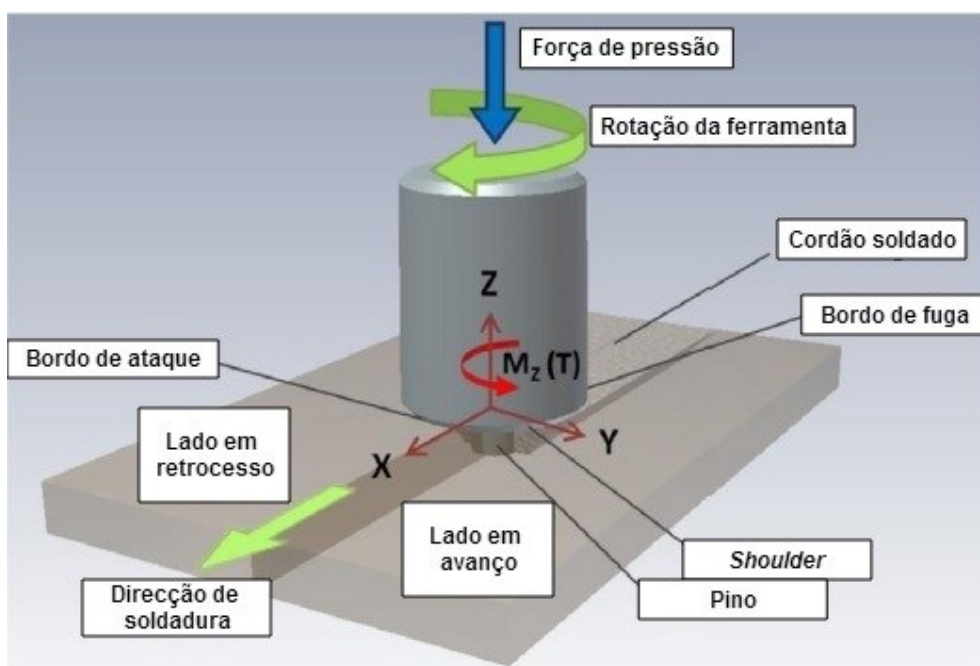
Processo de Soldadura por Fricção Linear, adaptado de [3].
